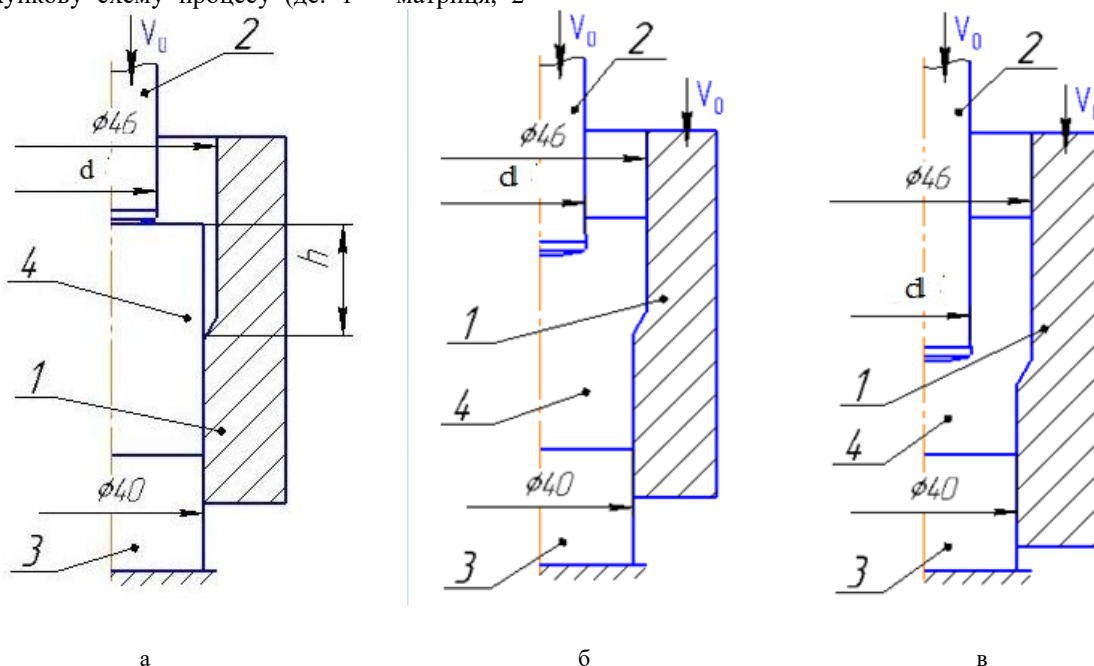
Розрахункова схема зворотного видавлювання з роздачою
